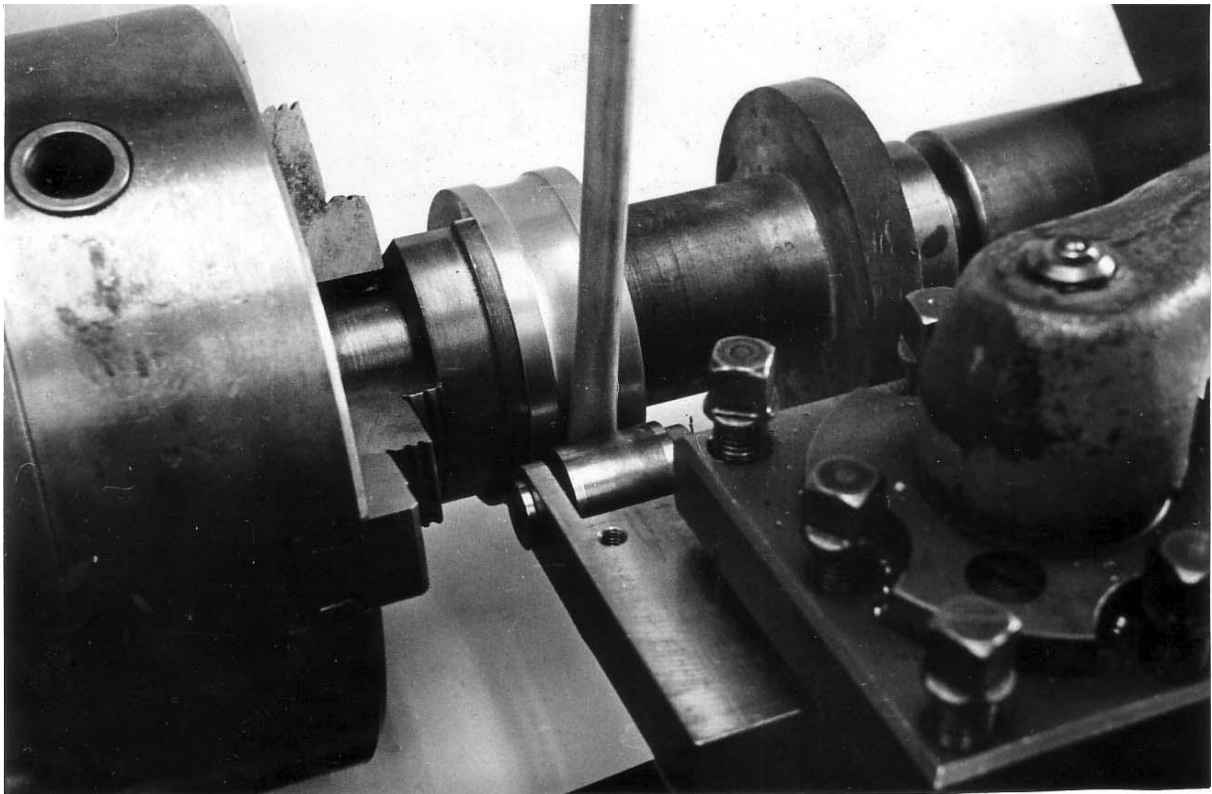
Операция предварительного сплющивания трубки заготовки
